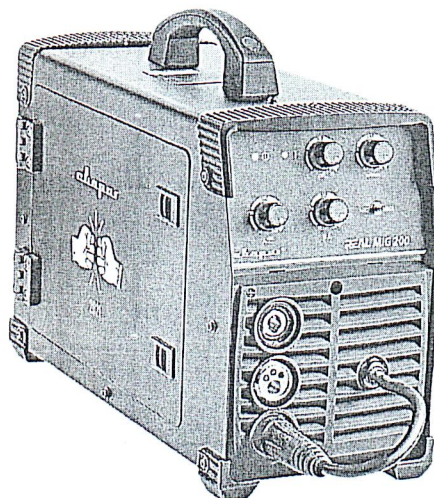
Полуавтомат Сварог REAL MIG 200 BLACK (N24002N)
